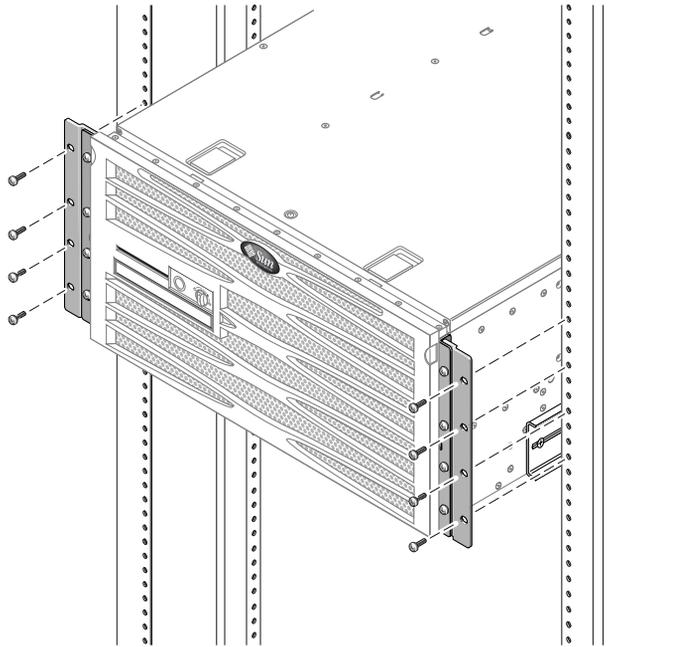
Montaje de los soportes de ajuste frontales de 600 mm en el bastidor
